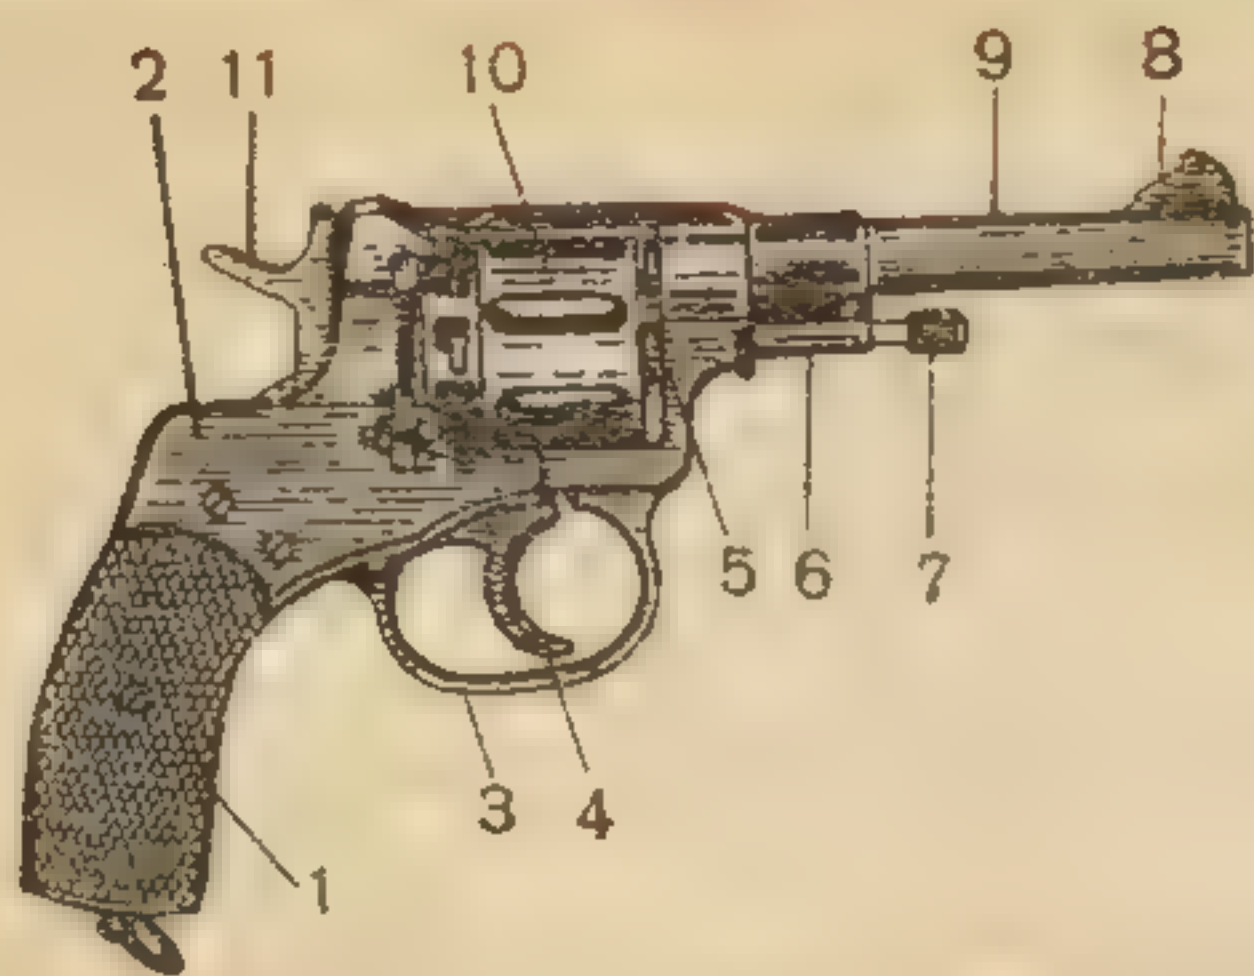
Револьвер «Наган» образца 1895 года (калибр 7,62 мм)
